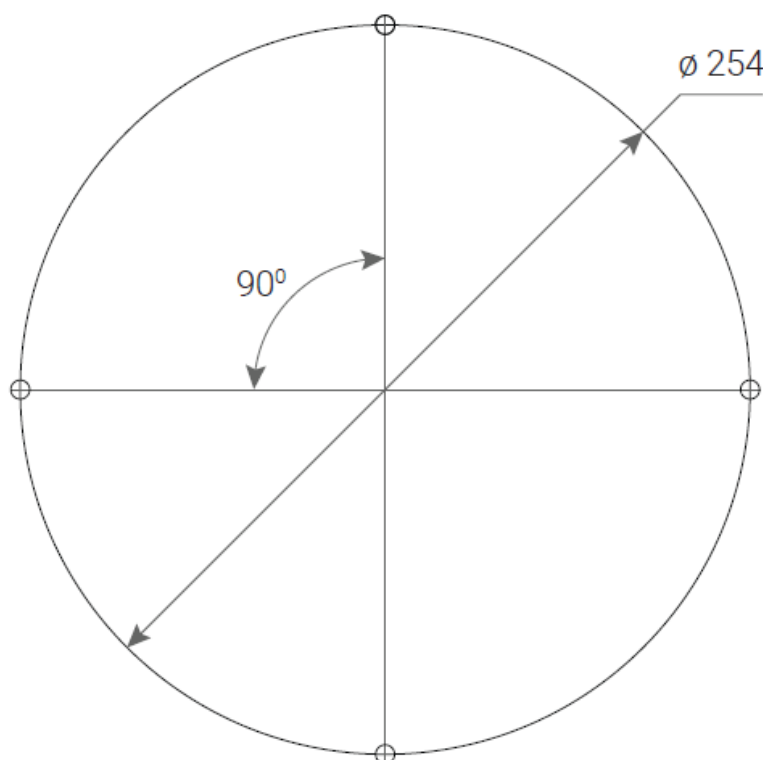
Схема разметки отверстий для монтажа манипулятора
